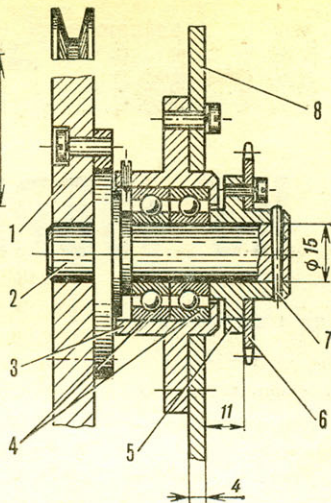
Подшипниковый узел рабочего колеса; 1 — кронштейн, 2 — шплинт, 3 — ось колеса, 4 — шайба, 5 — упорная втулка, 6 — подшипник № 204, 7 — ступица звездочки, 8 — звездочка, 9 — барабан колеса.
